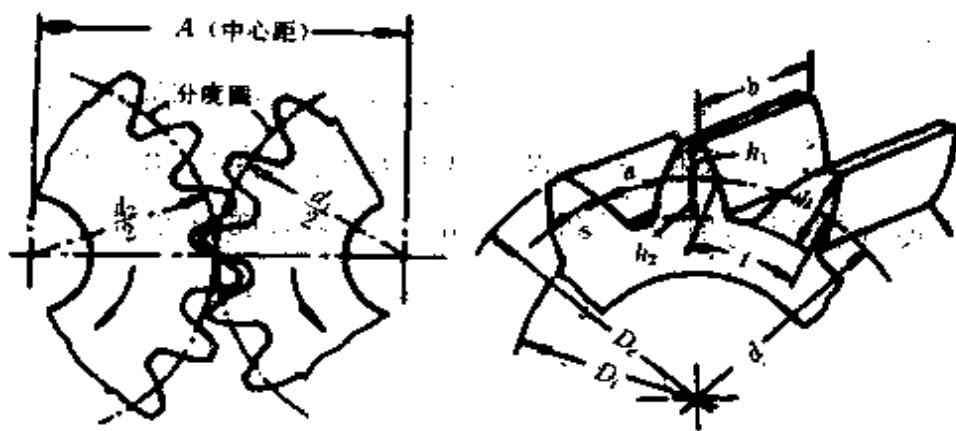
2 直齿圆柱齿轮的各部尺寸和啮合图
